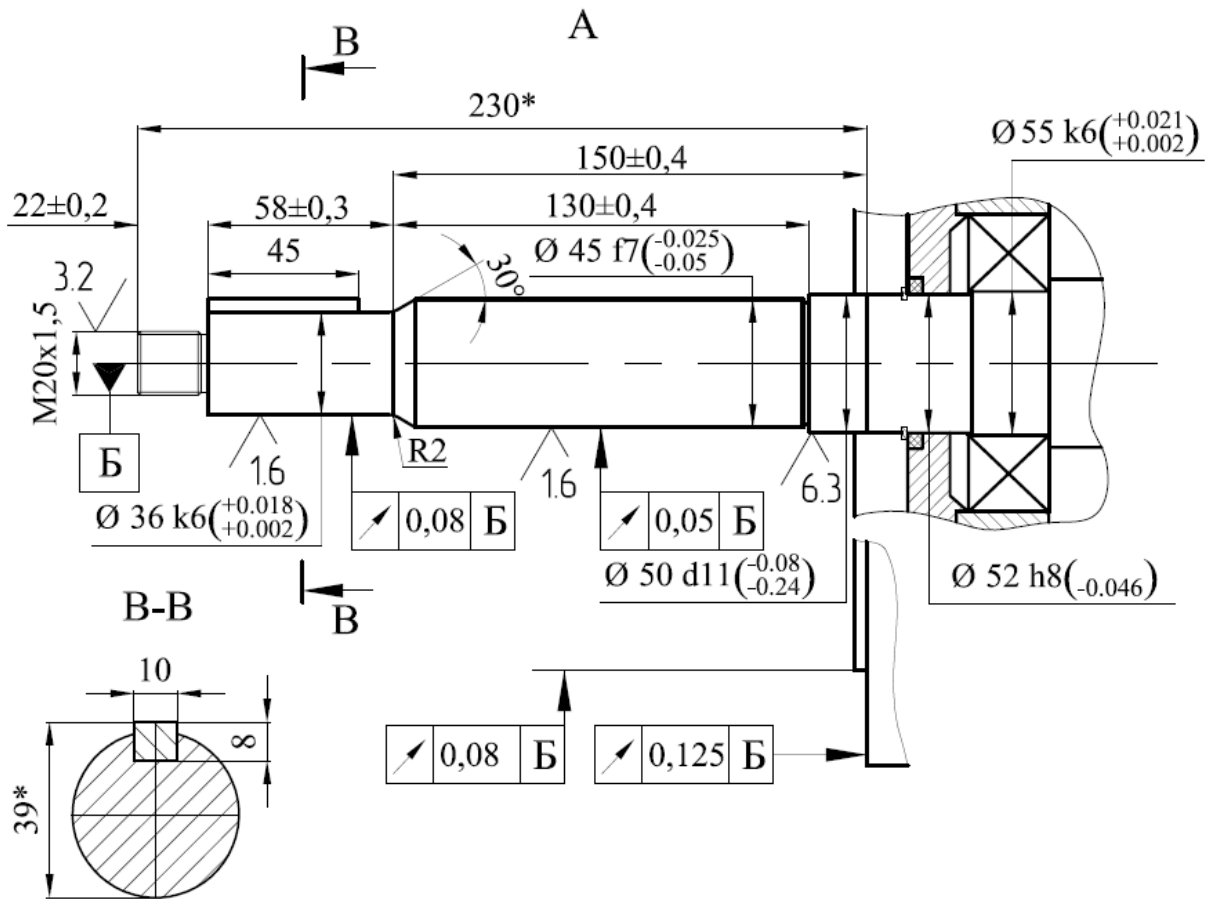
Свободный конец вала двигателя 6АМУ160М4ЖУ2
